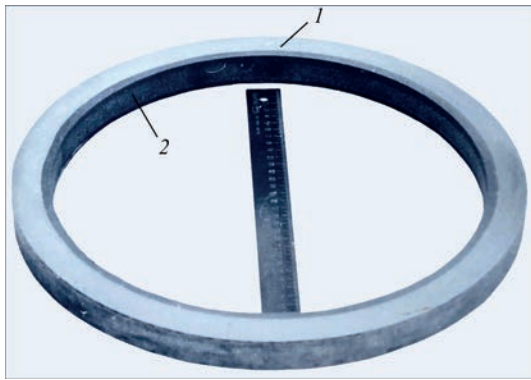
Макрошліф поперечного перерізу наплавленого валка стану 300: 1 – наплавлений шар; 2 – основний метал (внутрішня частина бочки валка видалена)
